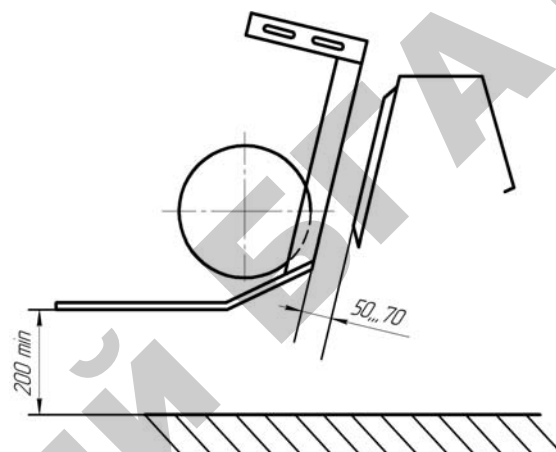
Установка зазора между ползками расстилочного барабана и склизом щитка
